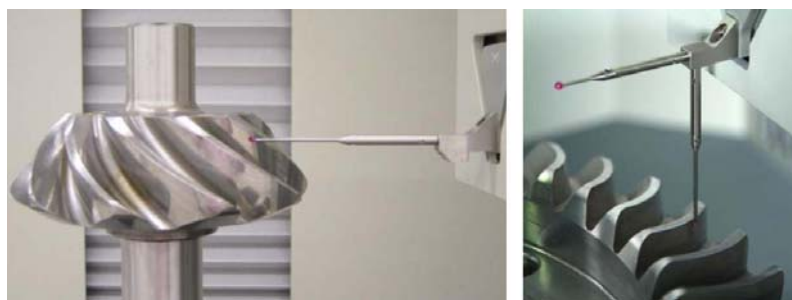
Mesure de flanc de denture sur une CMM [22]
